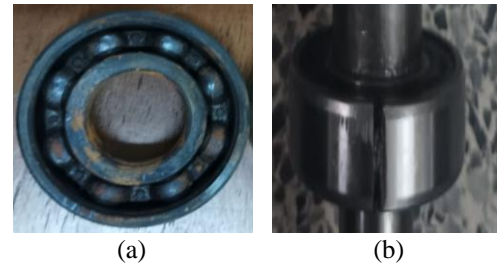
Rekonstruksi Bearing (a) Rusty Bearing; (b) Broken Bearing
